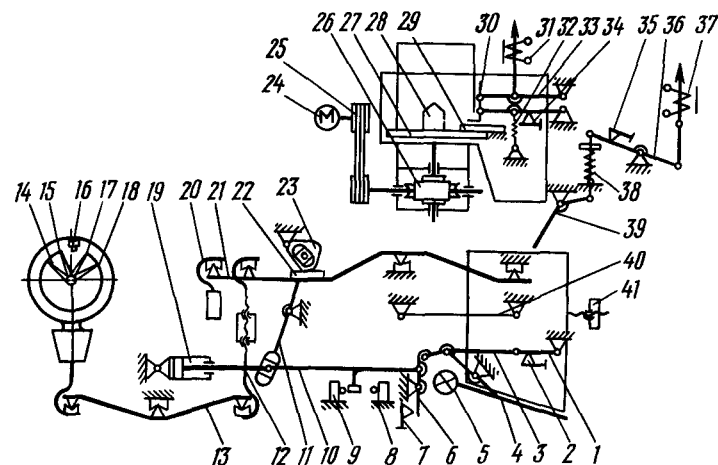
Кинематическая схема дозатора ДК-2:
